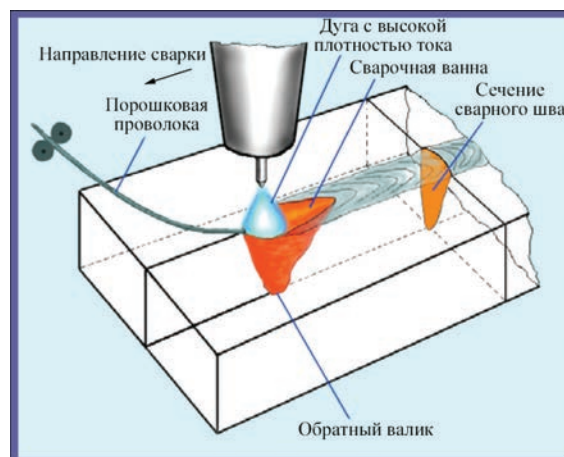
Схема TIG сварки с порошковой проволокой
